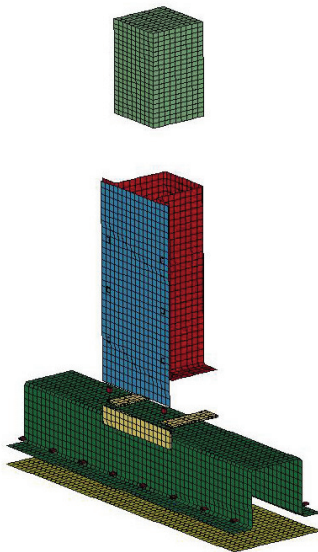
Isometrische Explosionszeichnung der verschiedenen T-Stoß-Teile
